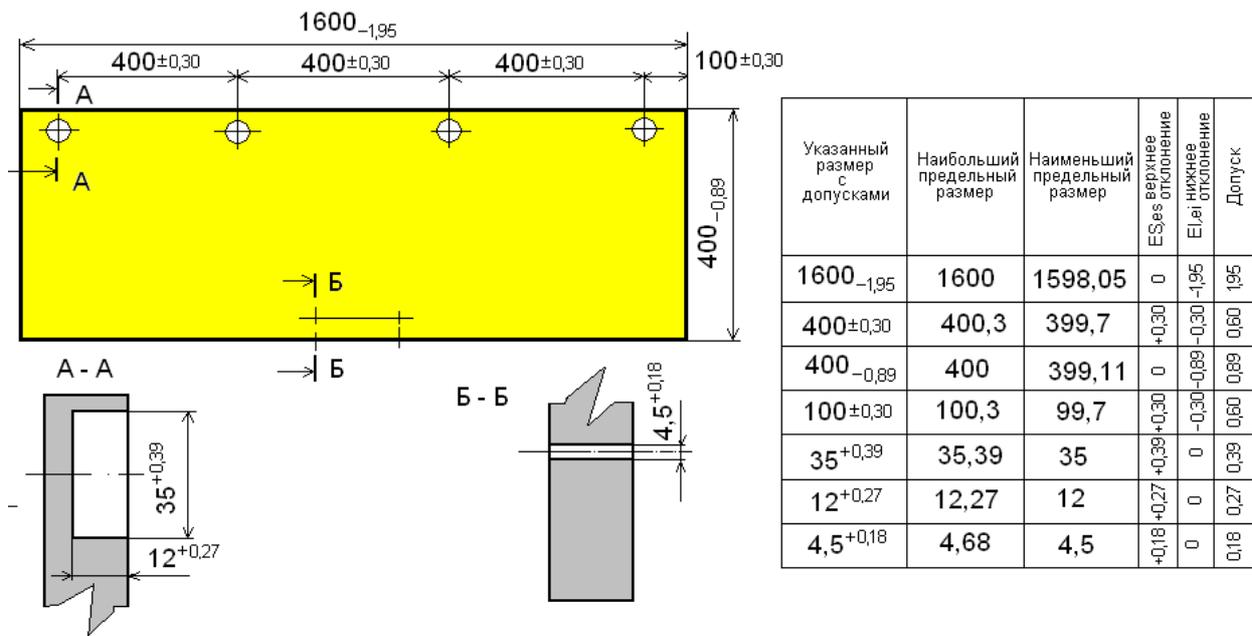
Чертеж дверки. Предельные размеры, верхние и нижние отклонения, величины допусков установленных размеров
